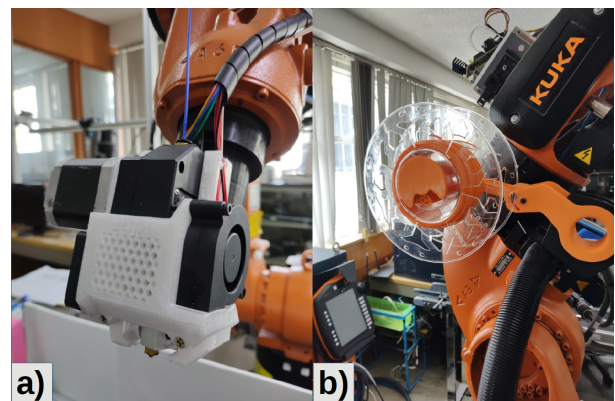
(a) Cabezal aditivo ensamblado con las piezas impresas en 3D, (b) Carrete de filamento y soporte impreso en 3D
